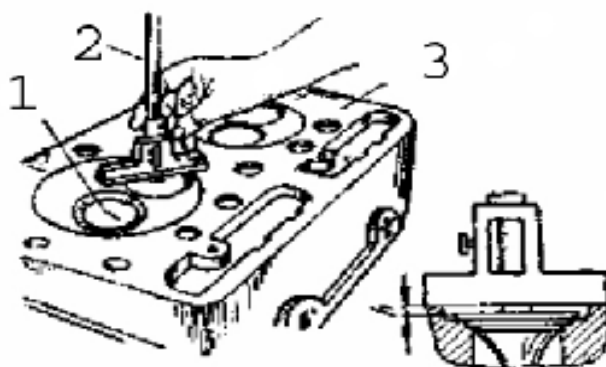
Вимірювання глибини заглиблення клапана: 1 – клапан; 2 – штангенглибиномір; 3 – головка блока
